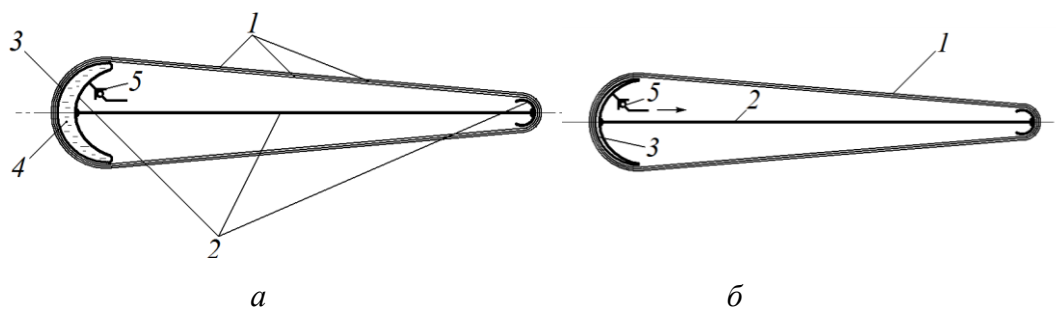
Шприцевальное устройство с ЭПФ: 1 – лентовидный РЭП из НТСП; 2 – жесткий корпус; 3 – труба из пластичного металла; 4 – гидравлическая жидкость; 5 – обратный клапан
